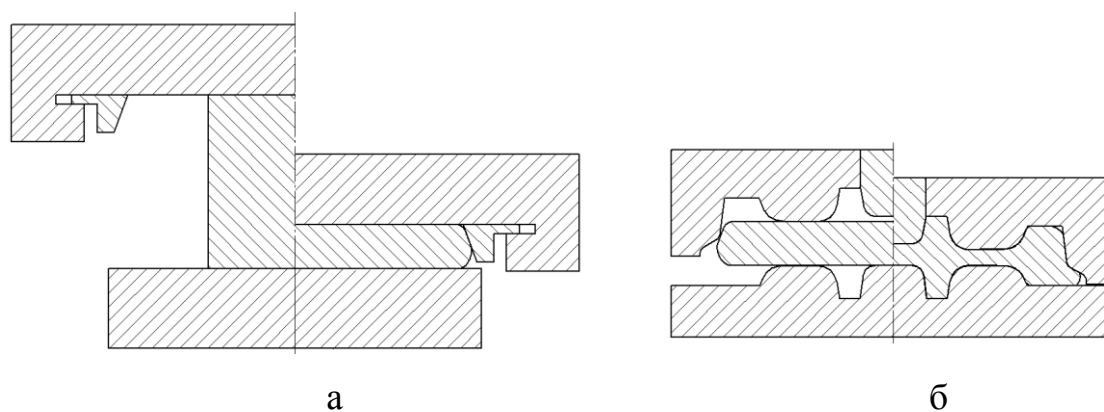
Действующая схема предварительной (а) и окончательной (б) штамповки на АО «ЕВРАЗ НТМК»
